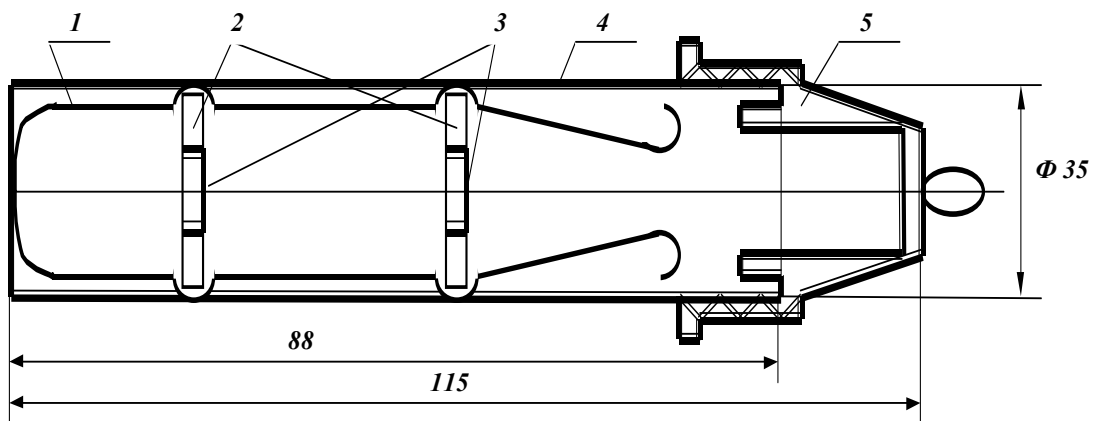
Схема пробоотборной камеры ИРР-3М. 1 – держатель пялец; 2 - пяльцы; 3 - детекторы; 4 - корпус; 5 – крышка.
